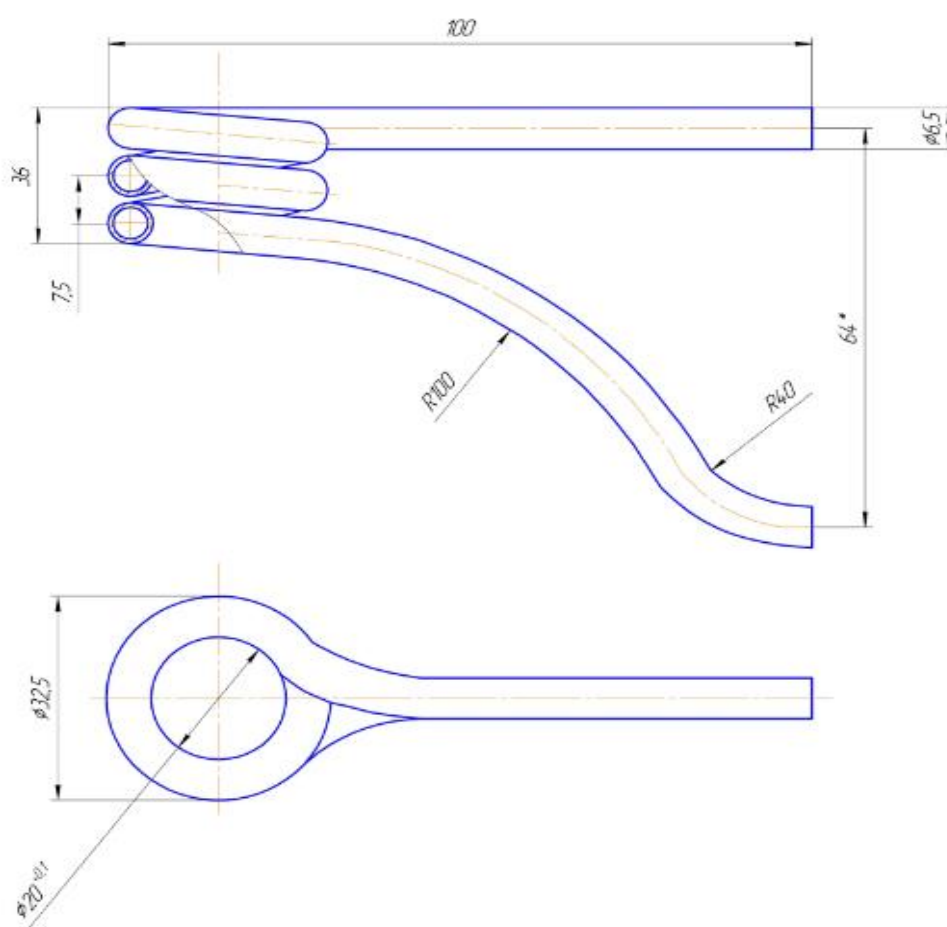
Конструируемый индуктор для нагрева образца
